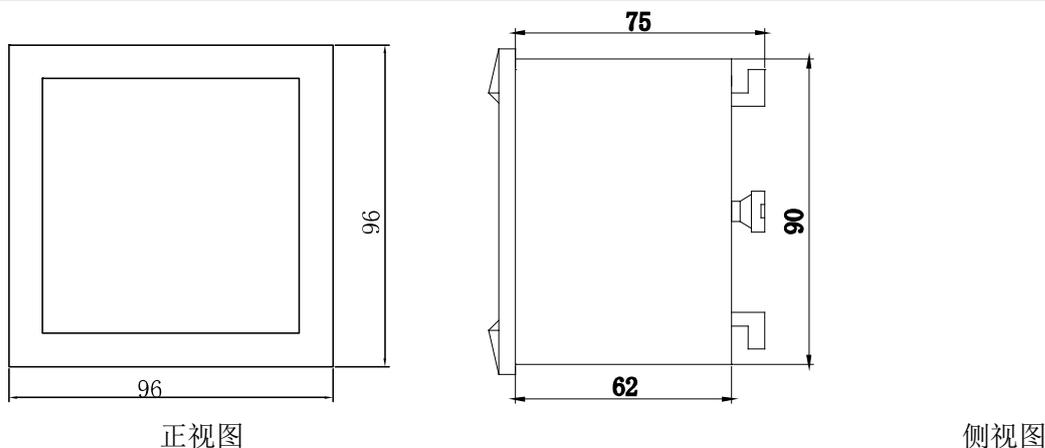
举例：96 型机械尺寸图 (单位: mm)
